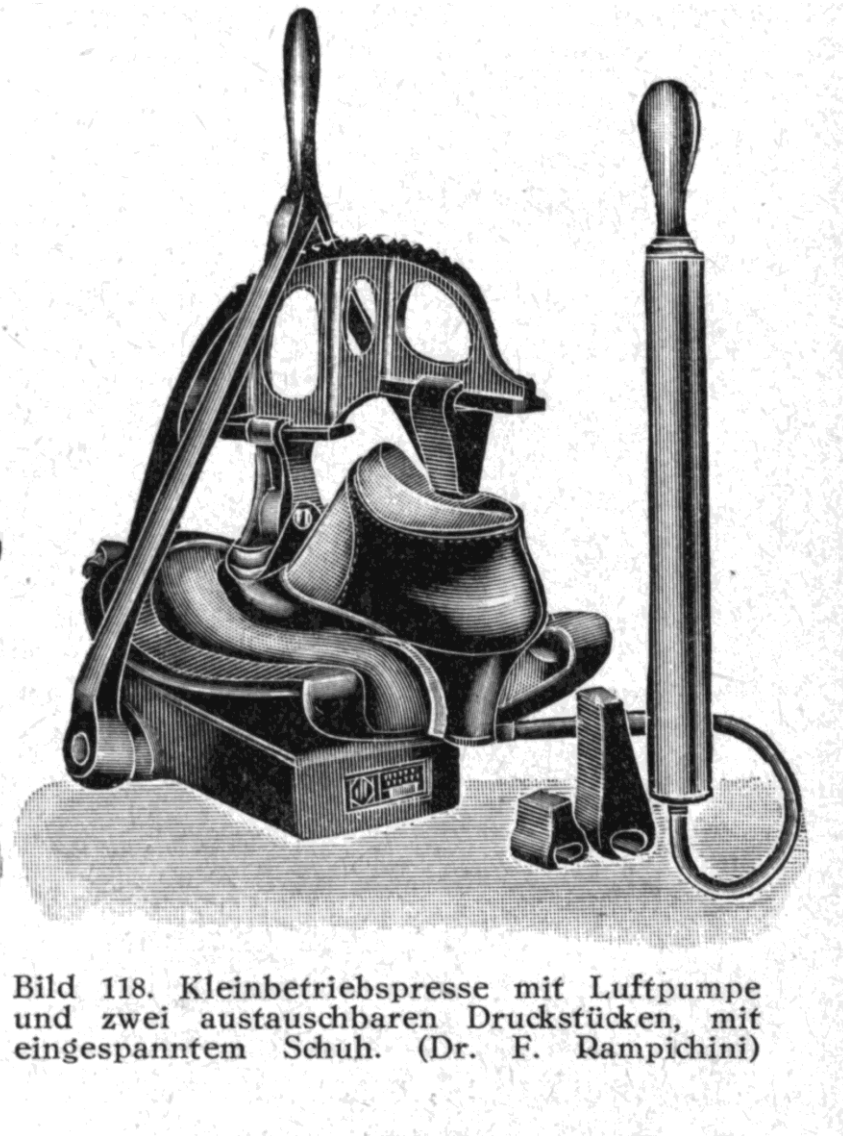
Kleinbetriebspresse mit Luftpumpe und zwei austauschbaren Druckstücken, mit eingespanntem Schuh. (Dr. F. Rampichini)
